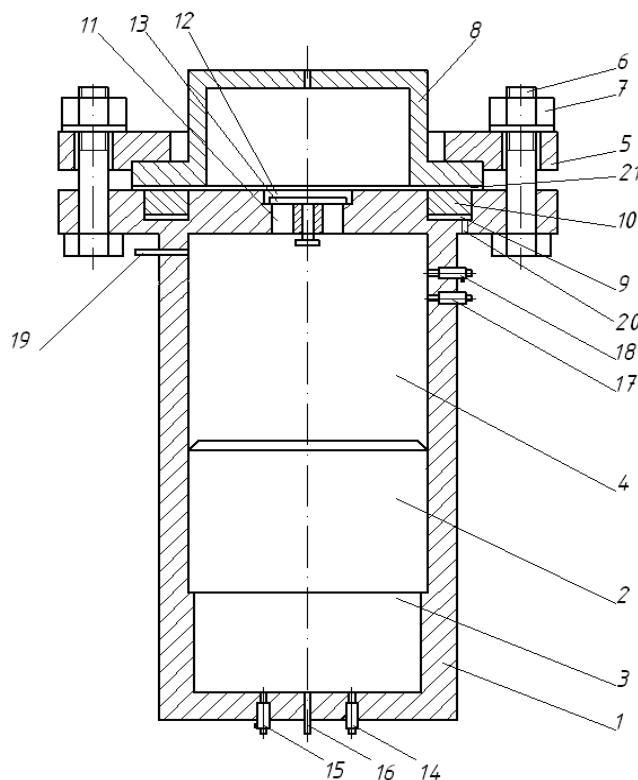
Схема двухкамерного устройства газовой штамповки:
